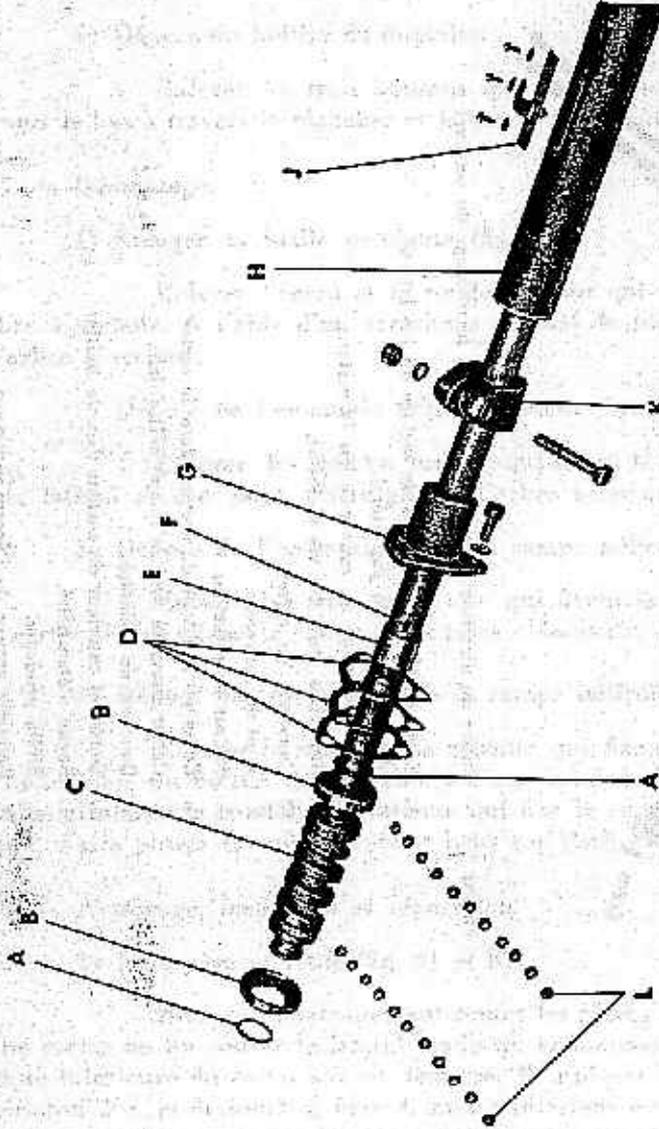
Ensemble arbre et rampe hélicoïdale (vue éclatée.)
